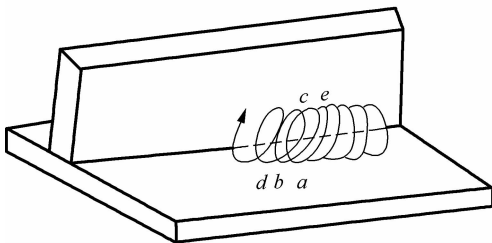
T 形接头角焊时的斜圆圈形运丝法
